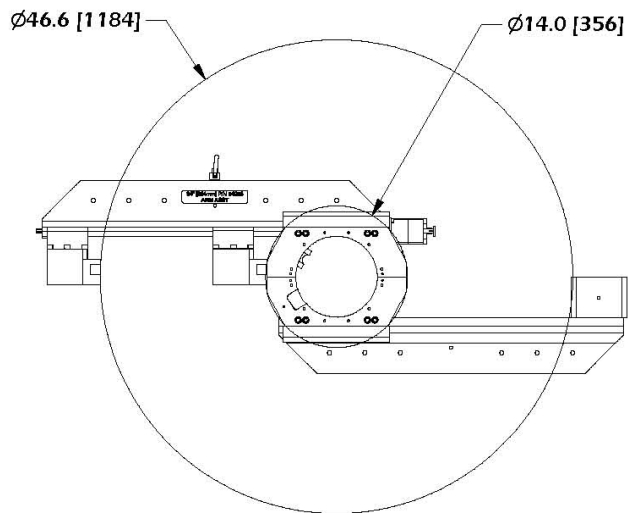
Dimensiones del conjunto de rodamiento sin alineación sin araña
